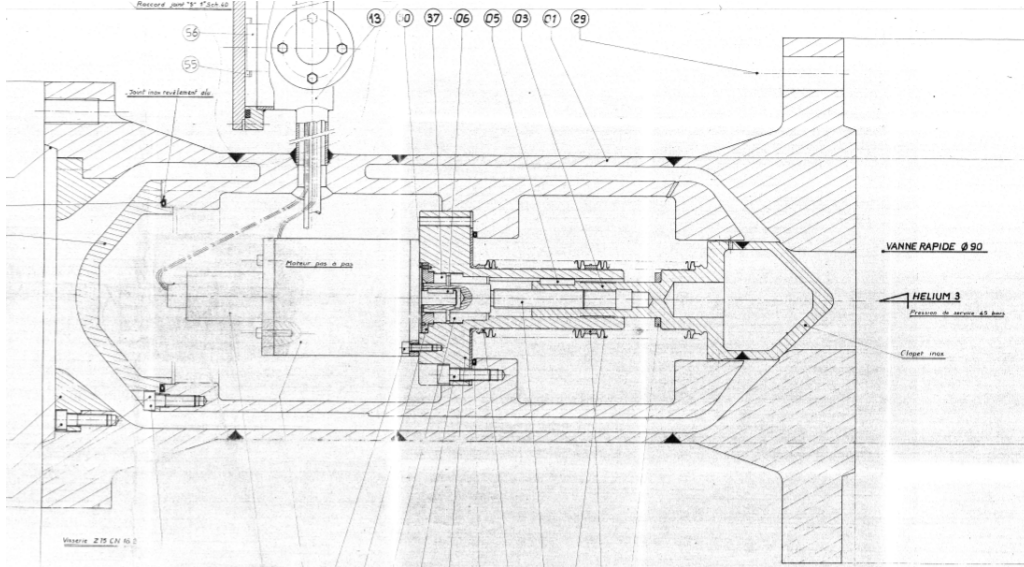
Extrait du plan de la VABT03 - coupe transversale
